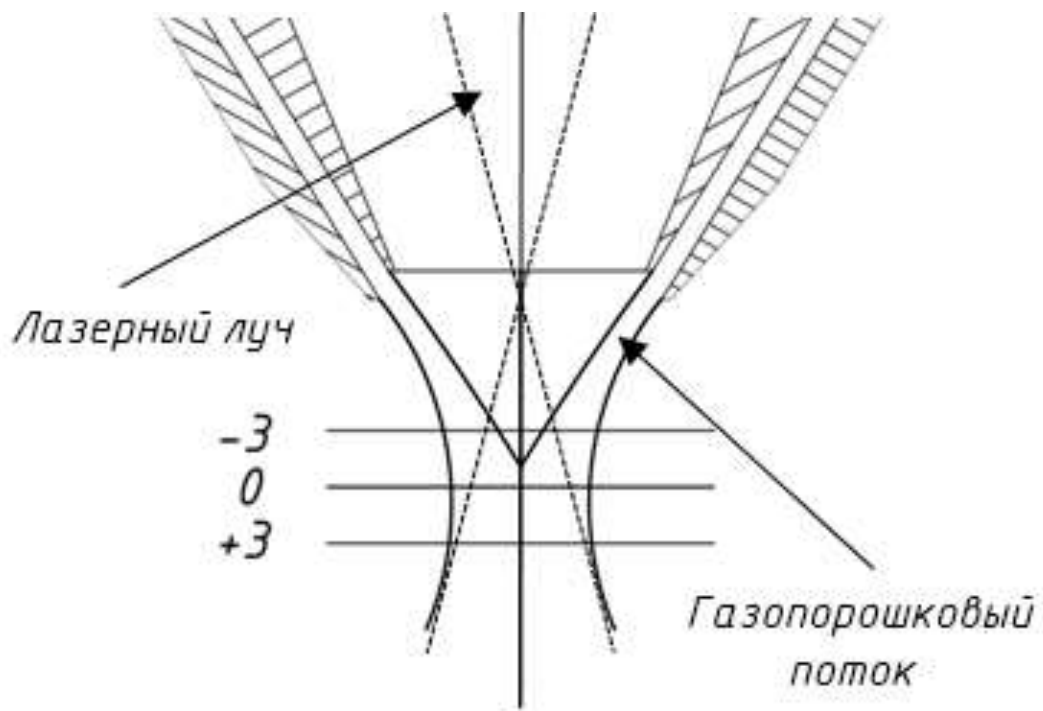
Схема положения фокуса газопорошкового потока относительно подложки: с заглублением фокуса ($F = -3 \text{ мм}$), с приподнятым фокусом ($F = +3 \text{ мм}$) и в фокусе газопорошкового потока ($F = 0$)
